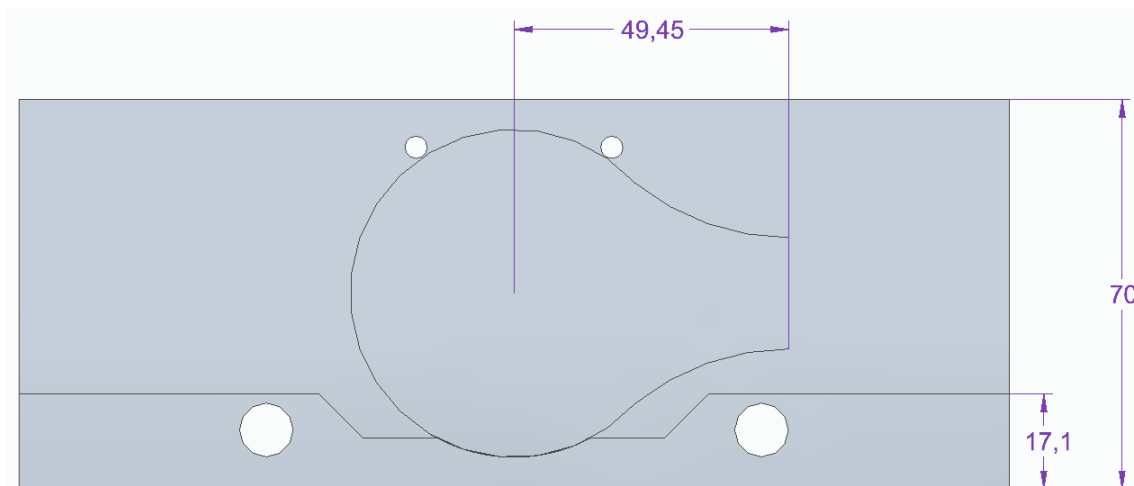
Alzado de la pieza base 2. Fuente: elaboración propia
